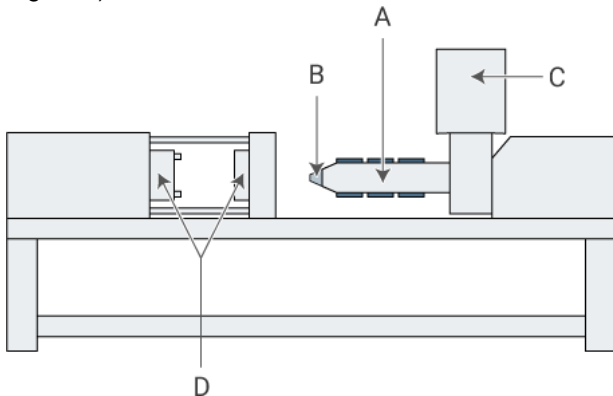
Estructura básica de las máquinas de moldeo por inyección
